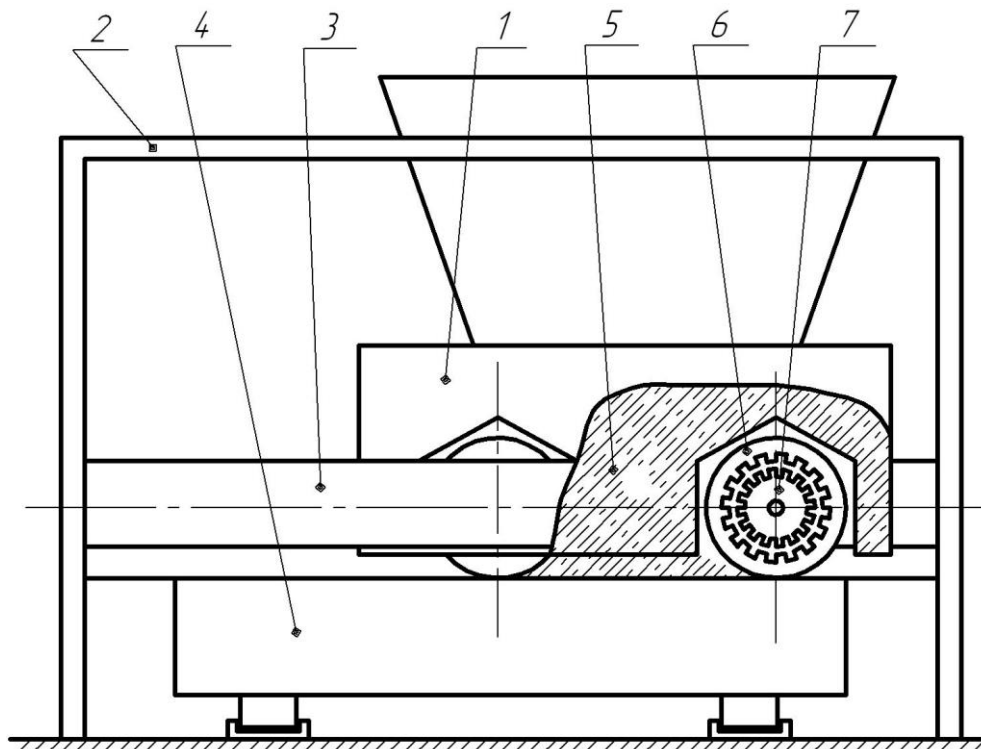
Роликова формувальна установка з приводом від крокового двигуна
